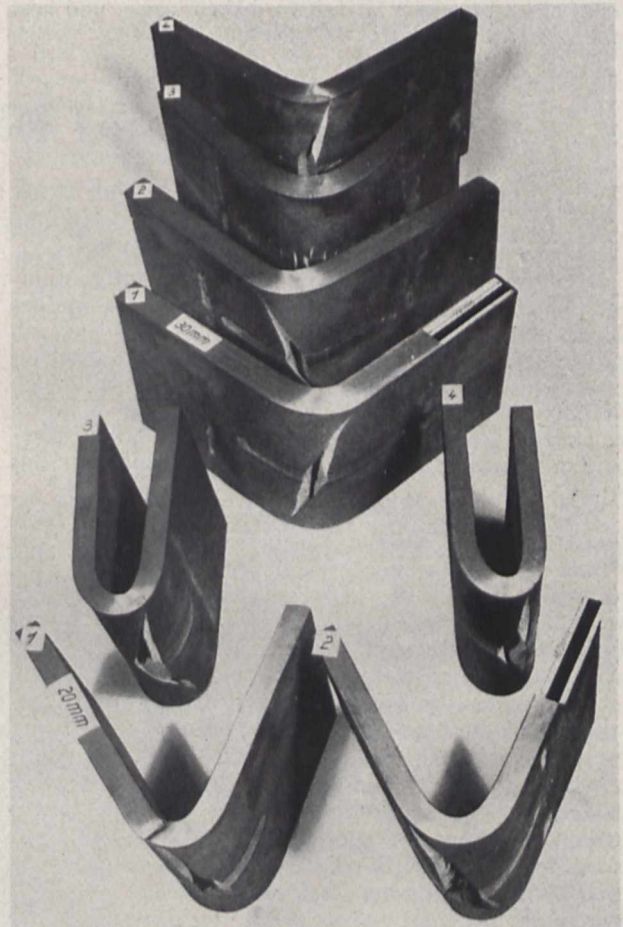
Aufschweißbiegeproben mit Silizium-Aluminiumberubigtem Thomas-Baustahl St 46. Blechdicke 20 und 30 mm
